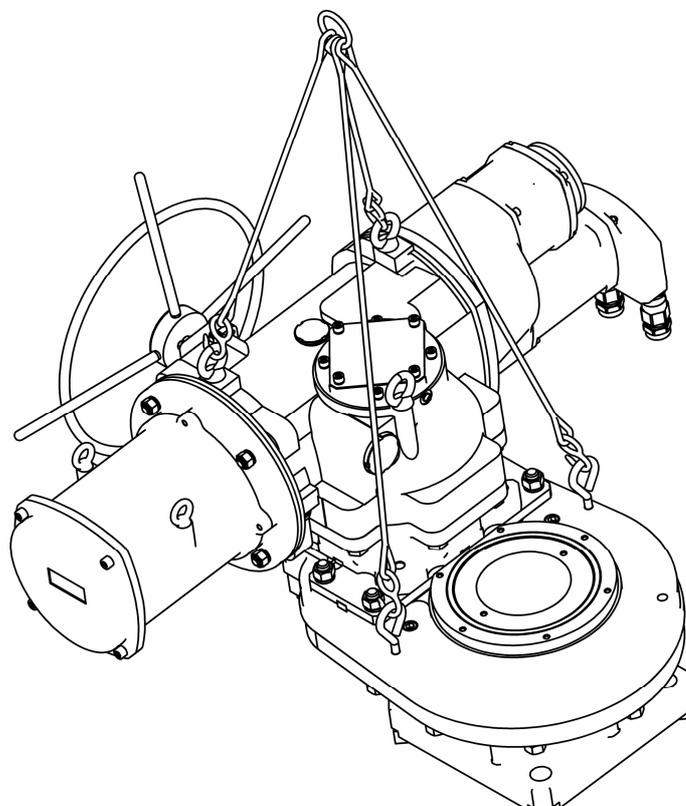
д – Схема строповки привода конструктивной схемы 430
